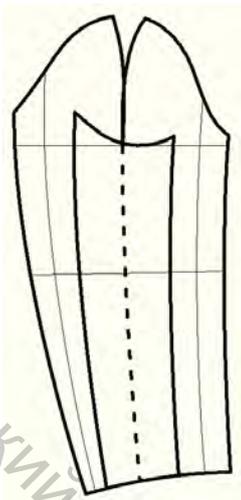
Чертеж типовой конструкции втачного трехшовного рукава
